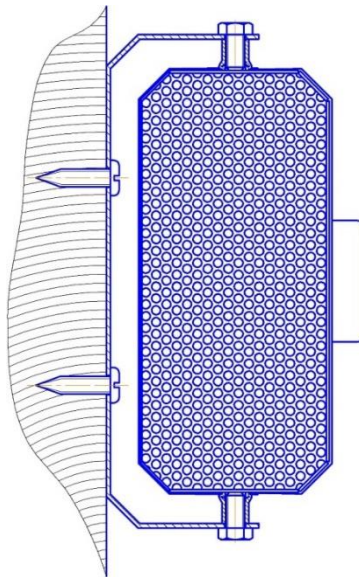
УГП в сборе с кронштейном, вид сверху
